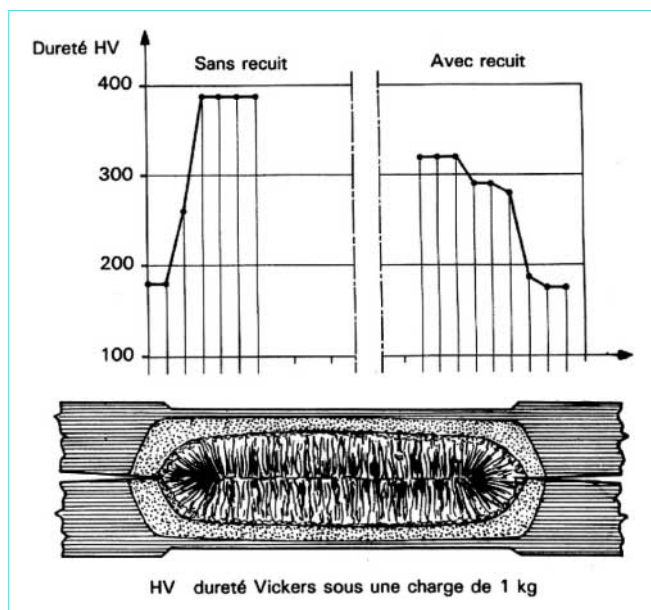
Soudage par points : dureté d'un point de soudure
